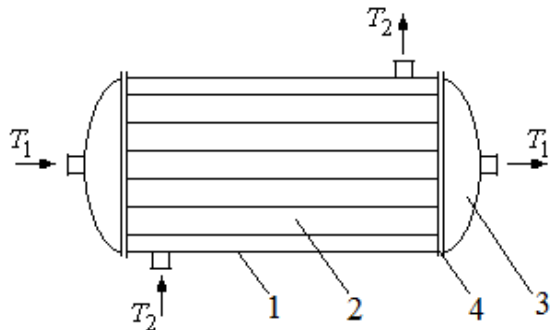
Схема кожухотрубчатого теплообменника: 1 – корпус; 2 – трубы; 3 – крышка; 4 – трубная решетка
